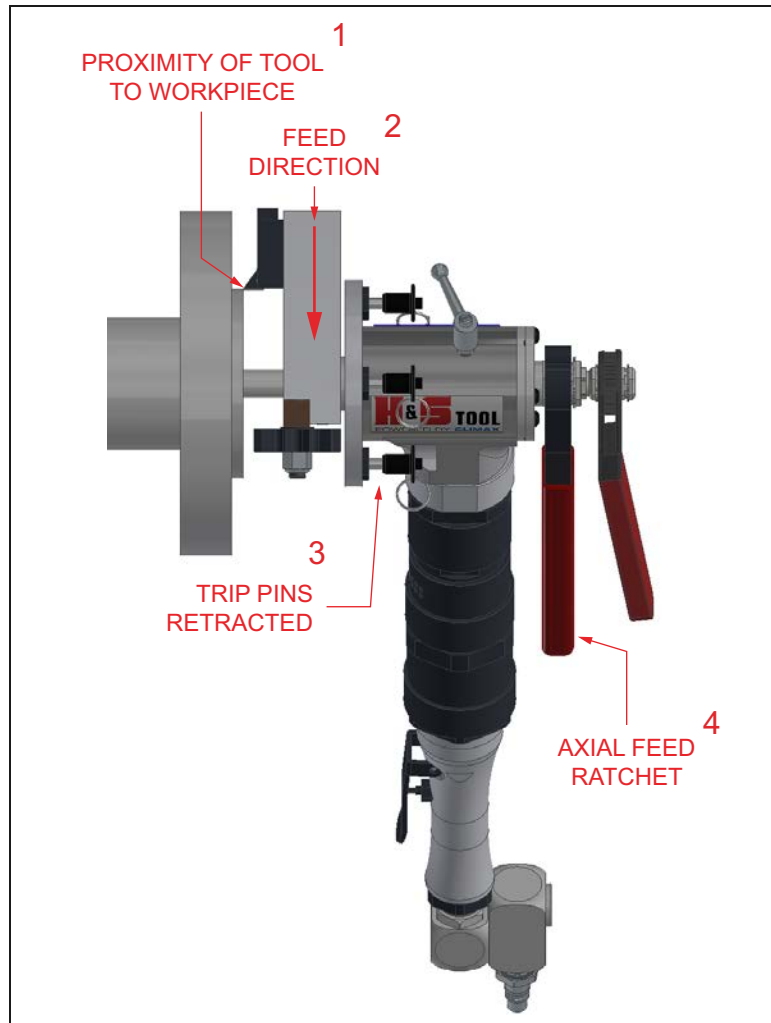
AVANCE AXIAL Y HERRAMIENTA TOCANDO LA PIEZA DE TRABAJO
